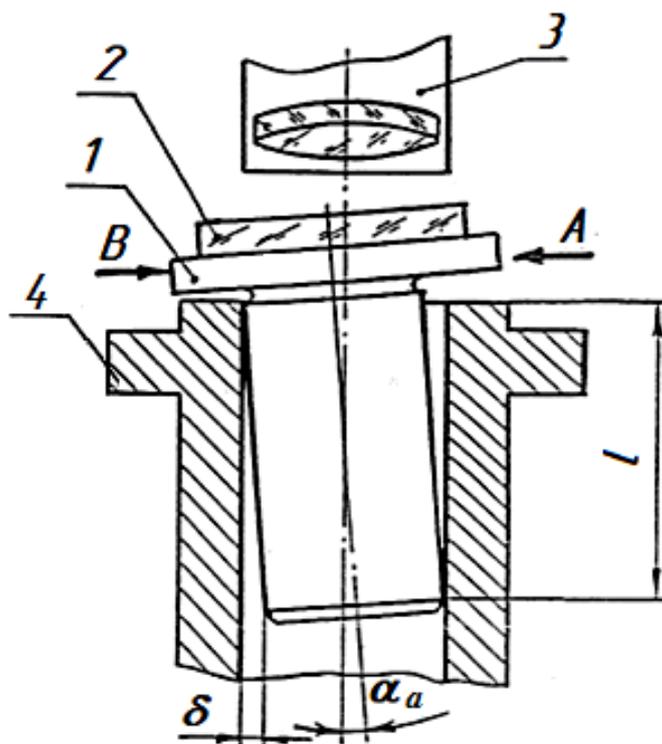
Схема контроля зазора в цилиндрических направляющих
